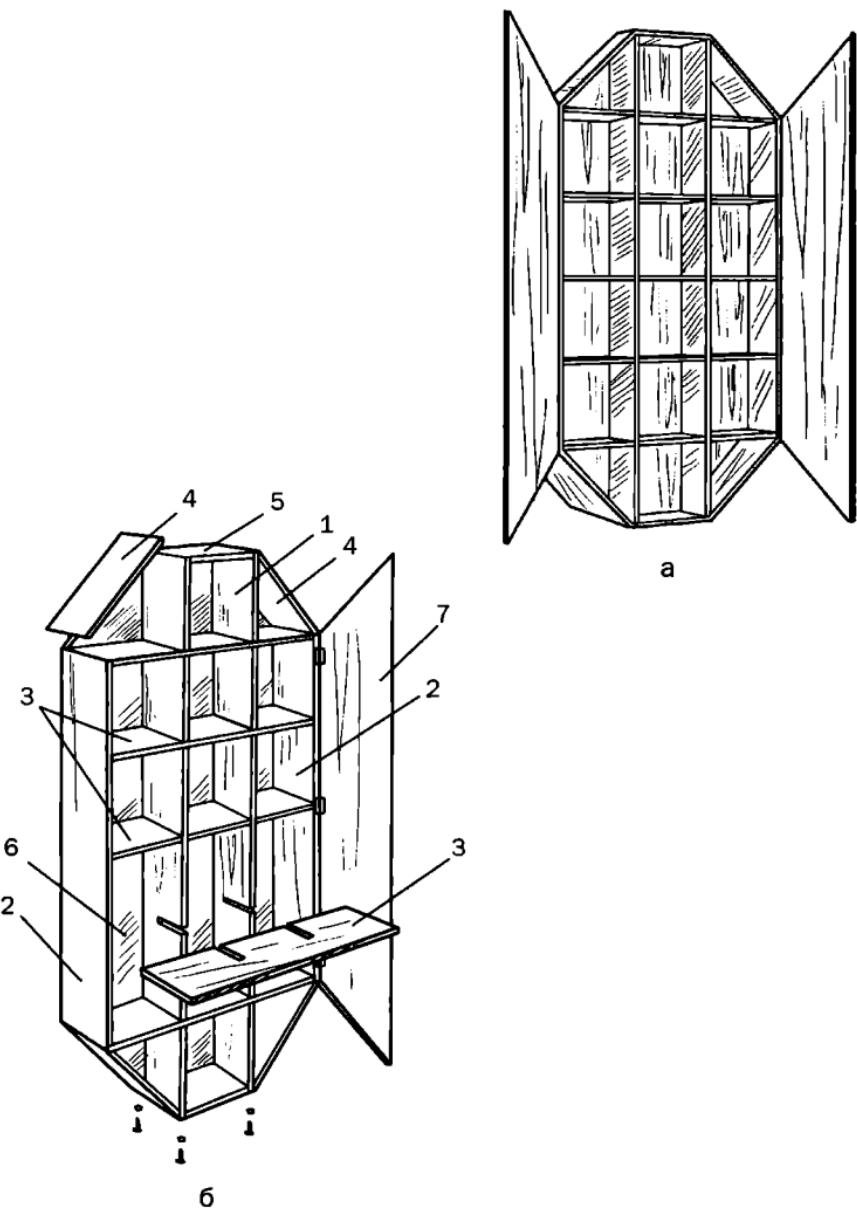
Кухонный стеллаж: а — общий вид; б — схема сборки:
